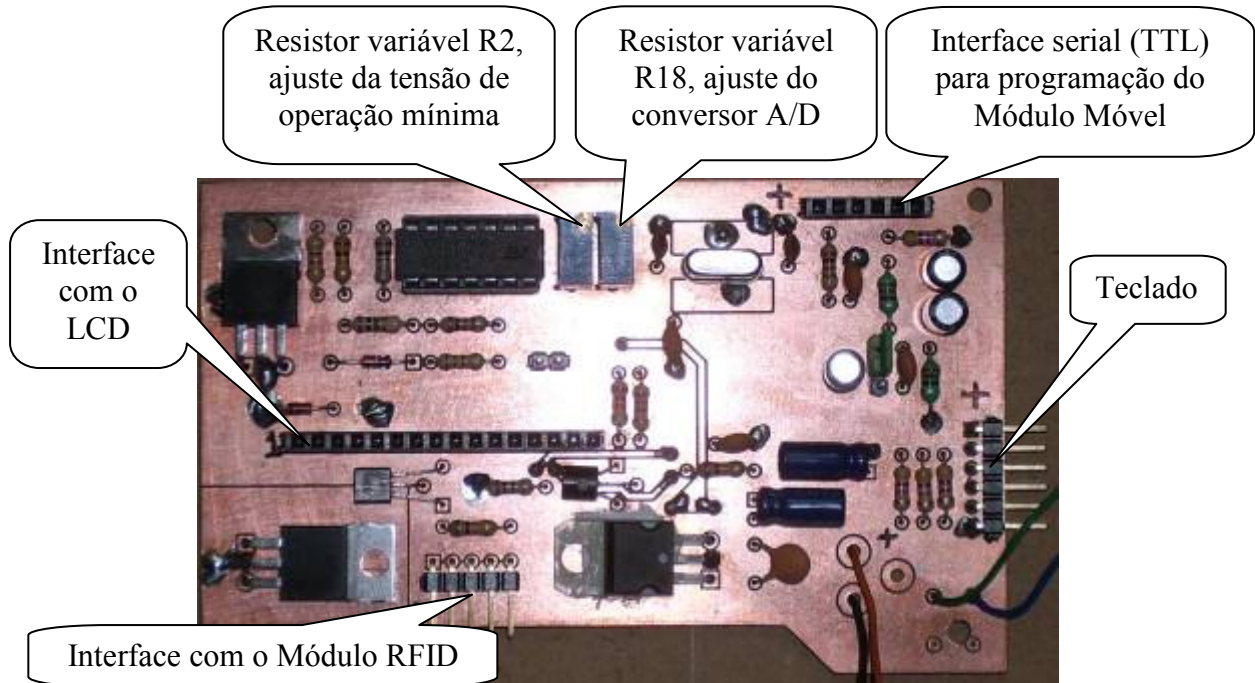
Face superior da placa do Módulo Móvel com componentes
